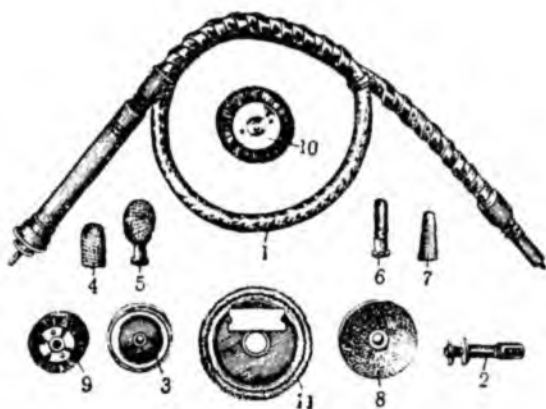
Гибкий вал с комплектом принадлежностей для шероховки:
